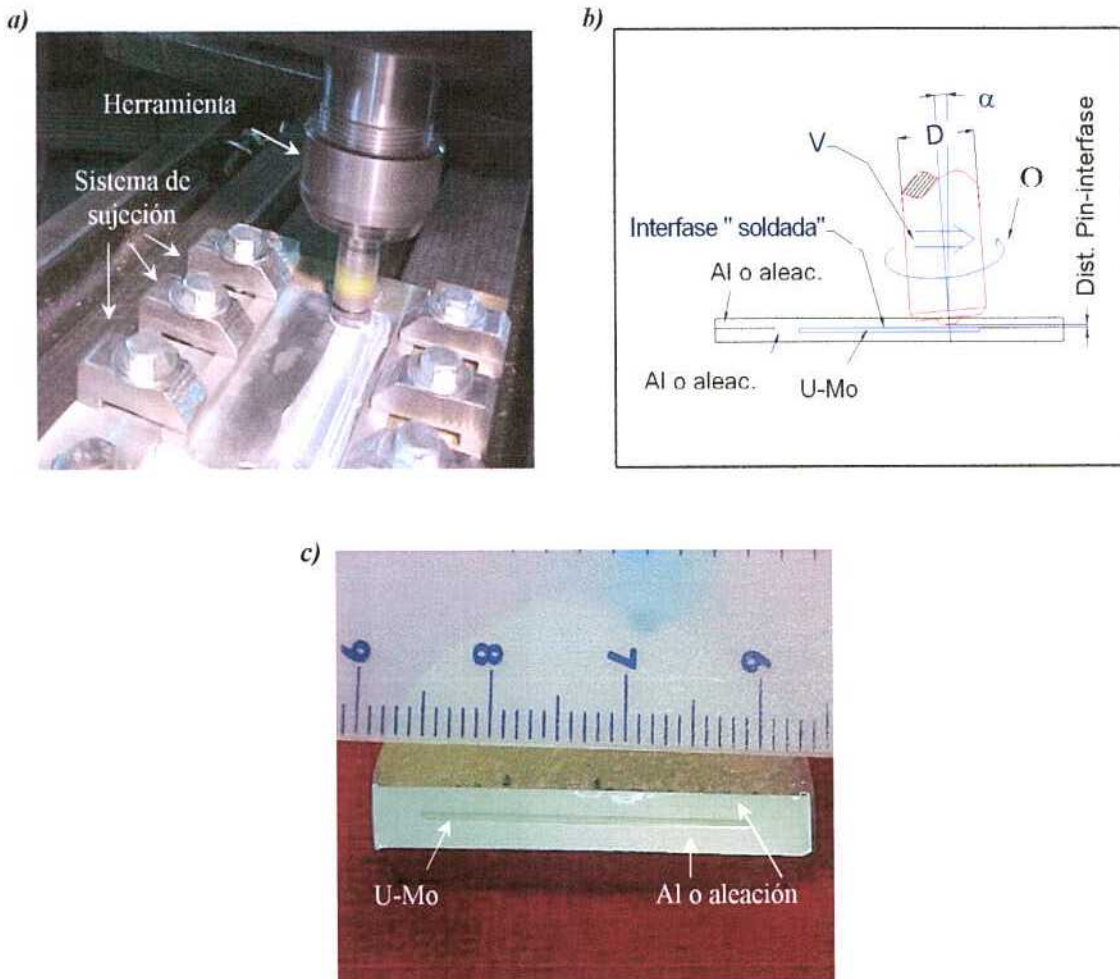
Fabricación de pares de difusión mediante el proceso de soldadura por fricción agitación (FSW). a) sujeción de todo el conjunto, b) esquema del proceso, c) corte transversal de uno de los pares.
